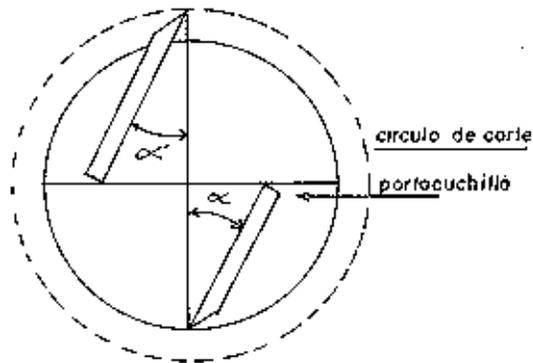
Ensayo de Moldurado en Cuchilla Sobresalida
